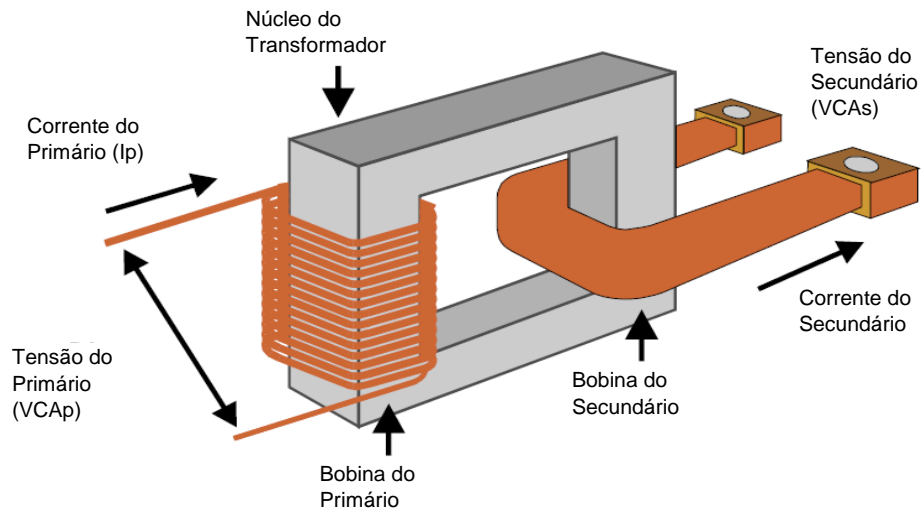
Representação esquemática dos principais componentes de um equipamento de soldagem por resistência elétrica.
